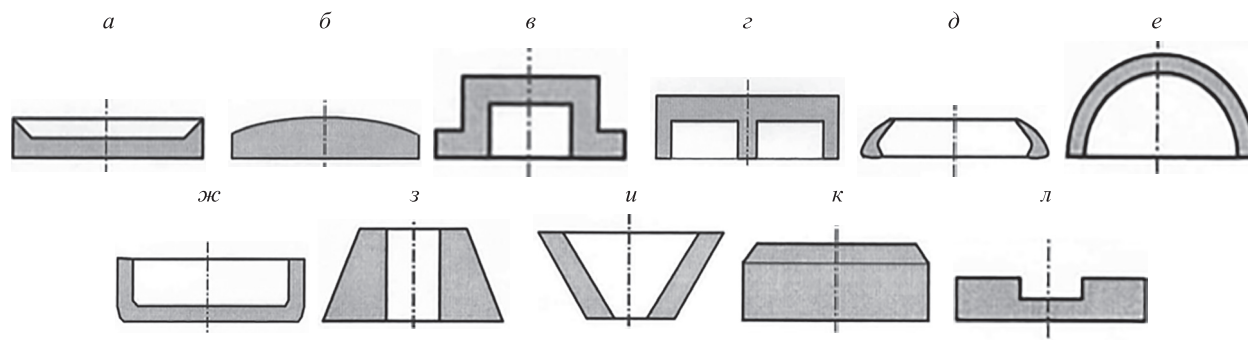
Виды специфических штучных деталей колпачкового подтипа: вогнутый (а); выпуклый (б); низкий (в); фигурный (г); кольцевой низкий (д); кольцевой высокий (е); чашеобразный (ж); конусный (з); профильный (и); совмещенный (к); таблетированный (л)
